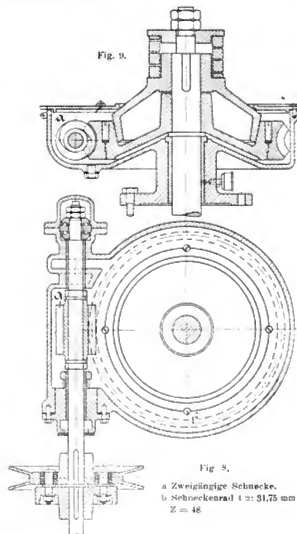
und 9. Schneckenkasten mit Motor- und Brems-
